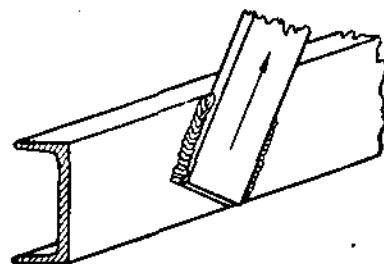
Образец, в котором сварные швы подвергаются срезывающим усилиям.
